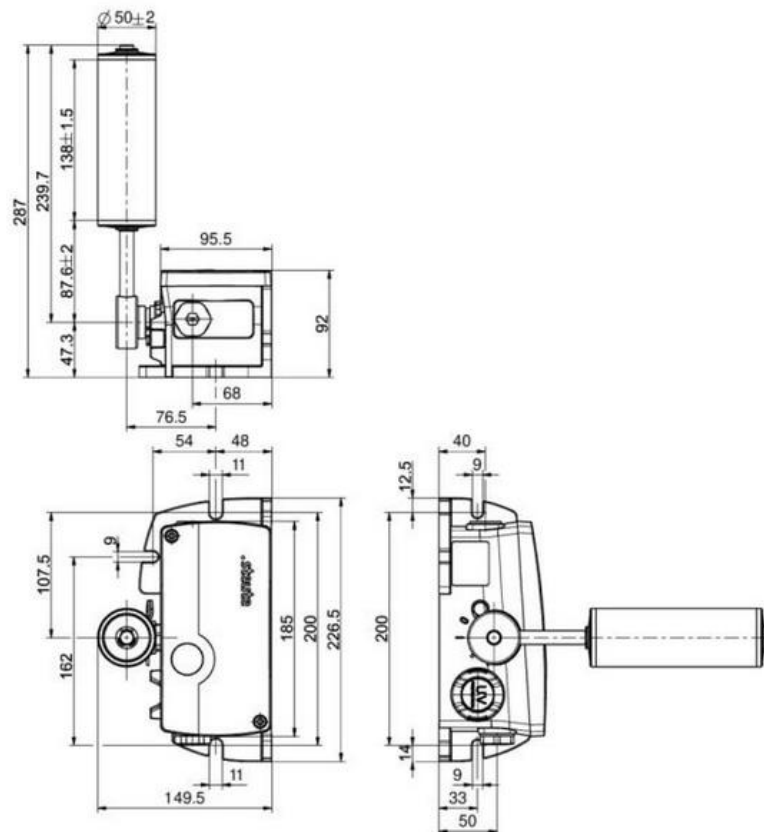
Габаритне креслення датчика сходження стрічки Steute ZS 92
